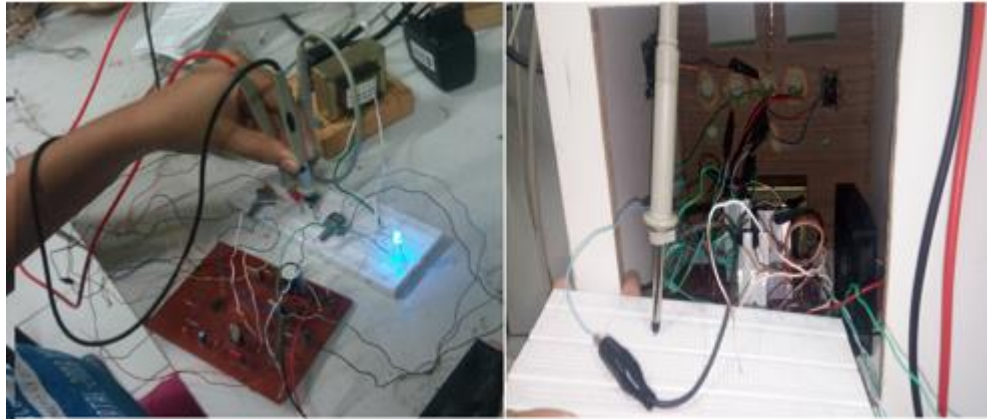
PCI do setup com as trilhas estanhadas e componentes inseridos e soldados.
